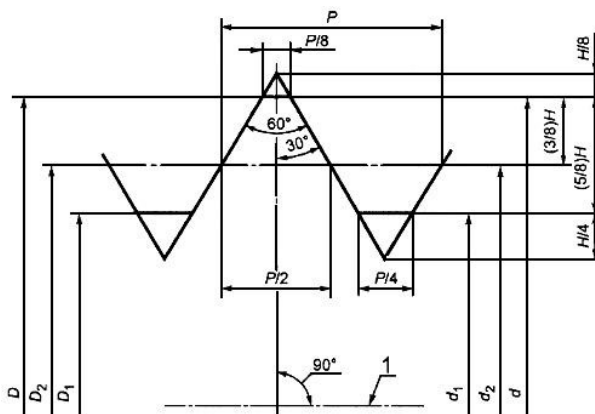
Основной профиль метрической резьбы: 1 - ось резьбы
